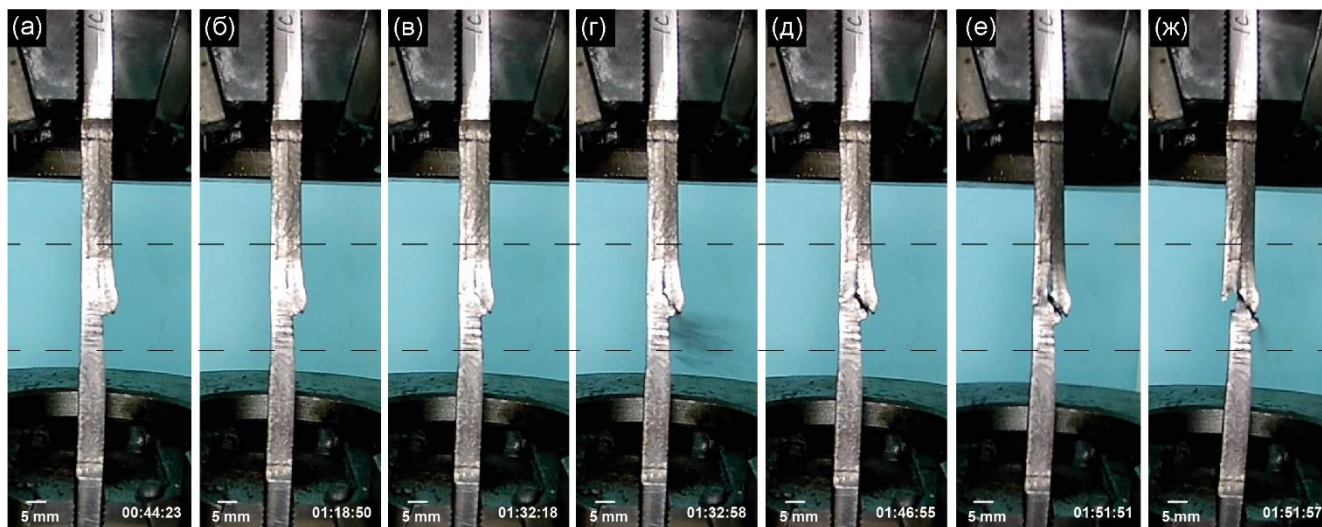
Динамика разрушения образца с дефектами (а – без видимых разрушений; б – зарождение трещины со стороны валика шва; в – развитие трещины; г – разрыв по сварному шву напротив одного из слоев; д – зарождение трещины с противоположной стороны образца; е – отрыв по внешнему слою и зарождение трещины по центральному слою; ж – разрушение образца)
